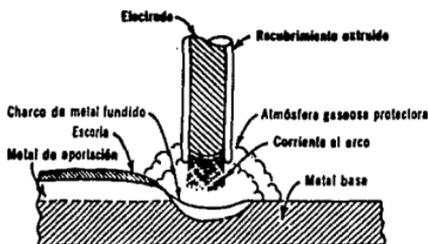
Proceso de Soldadura de Arco Protegido.
